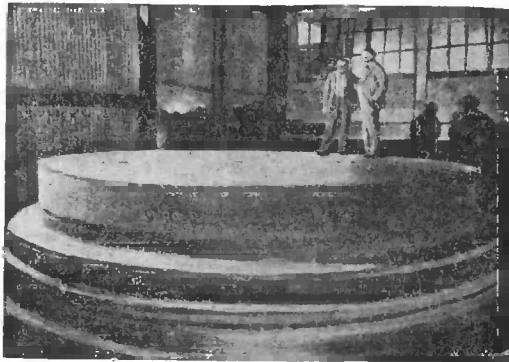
Форма для отливки 120-дюймового зеркала.
